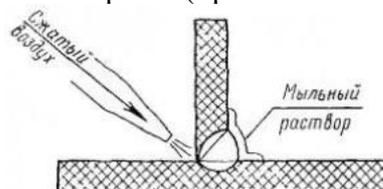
Проверка обдувом сварных соединений воздухом
